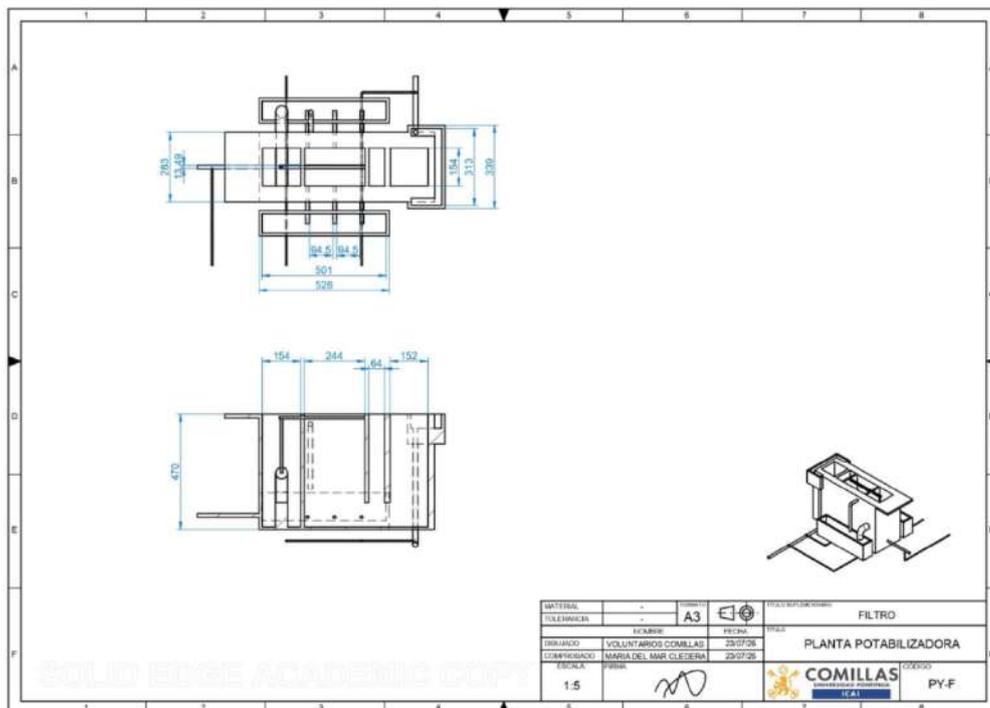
Plano descriptivo de la planta con acotaciones
